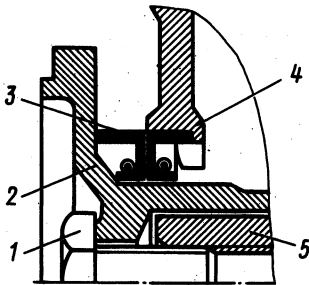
Запрессовка сальника коленчатого вала двигателя МеМЗ без разборки двигателя:
